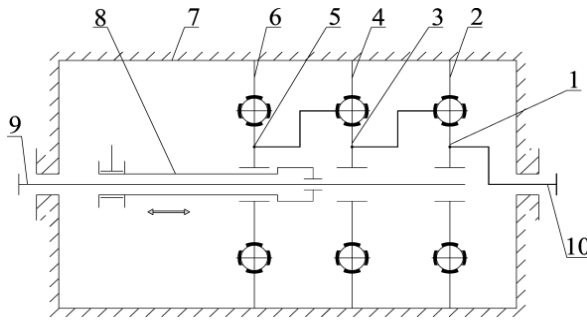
Кинематическая схема механизма ШПФМ
